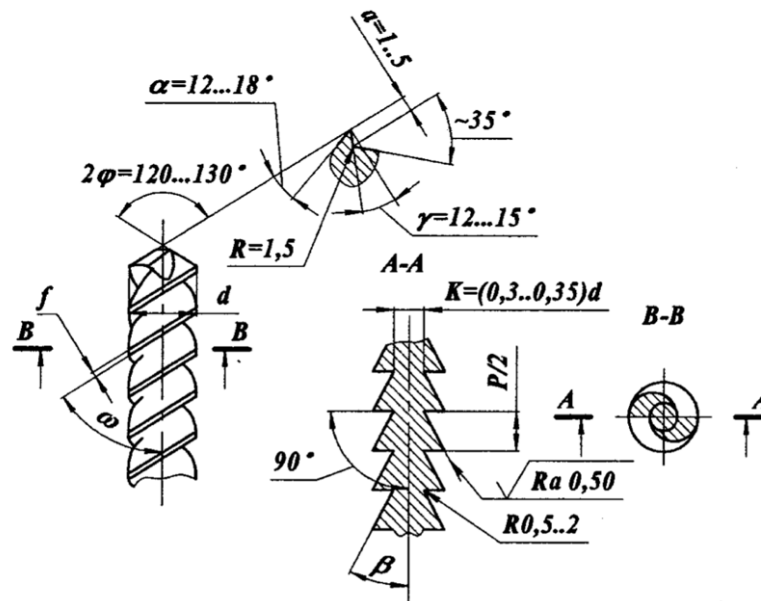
Елементи конструкції та геометрії шнекового свердла для обробки чавуну
